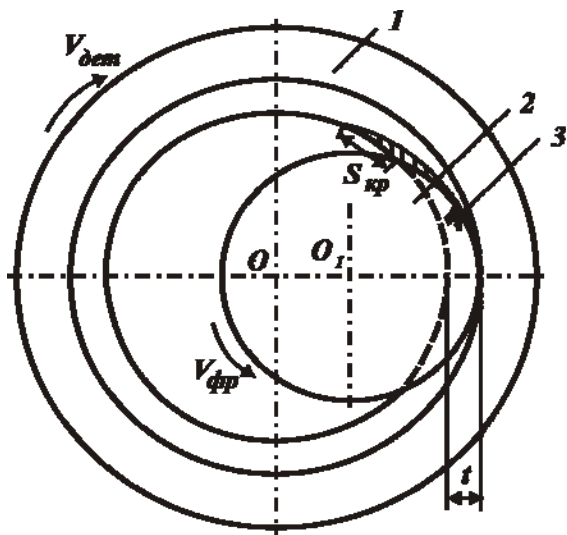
Расчетная схема расфрезеровывания отверстия: 1 – обрабатываемое кольцо; 2 – фреза; 3 – зуб фрезы
